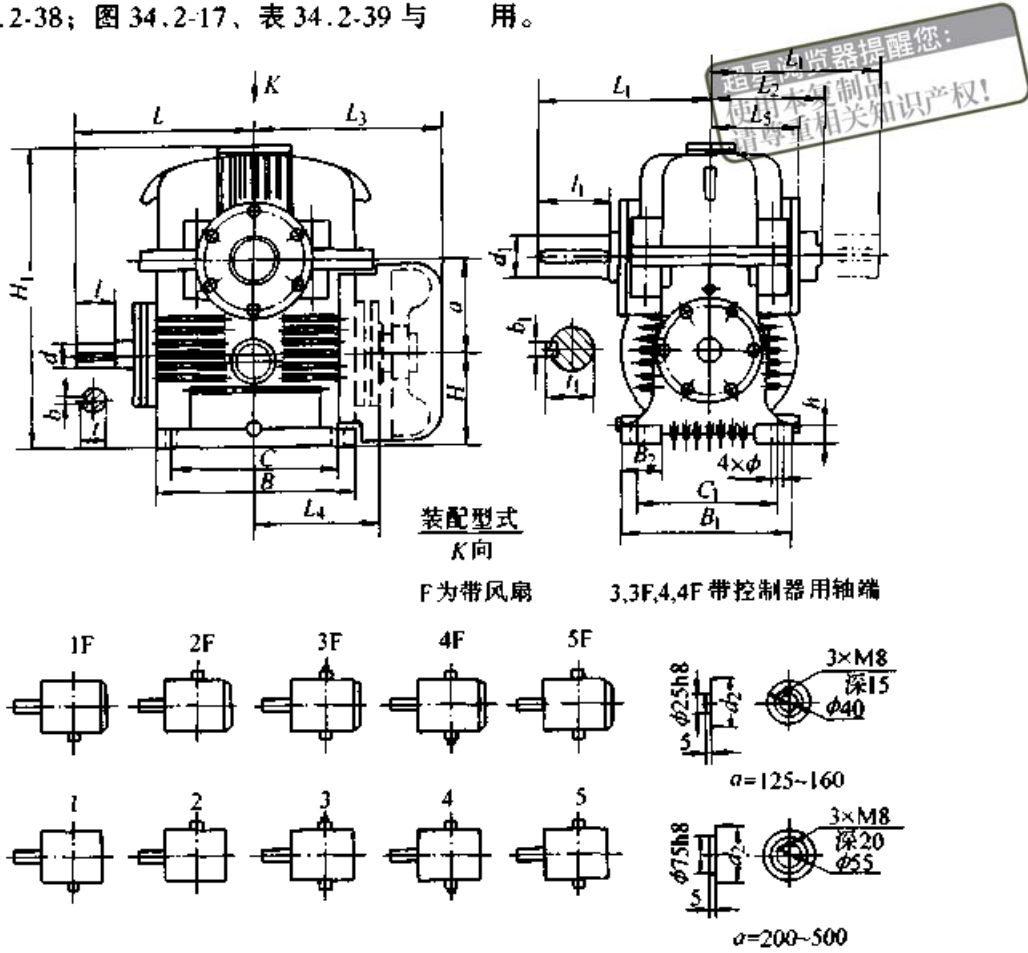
TPU 型减速器外形尺寸及装配型式
